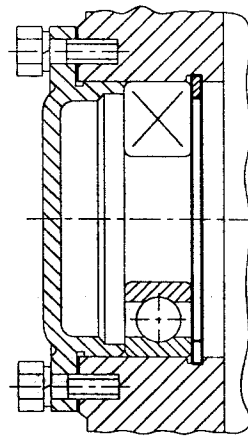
Закрепление наружного кольца подшипника качения в корпусе с использованием пружинного кольца
